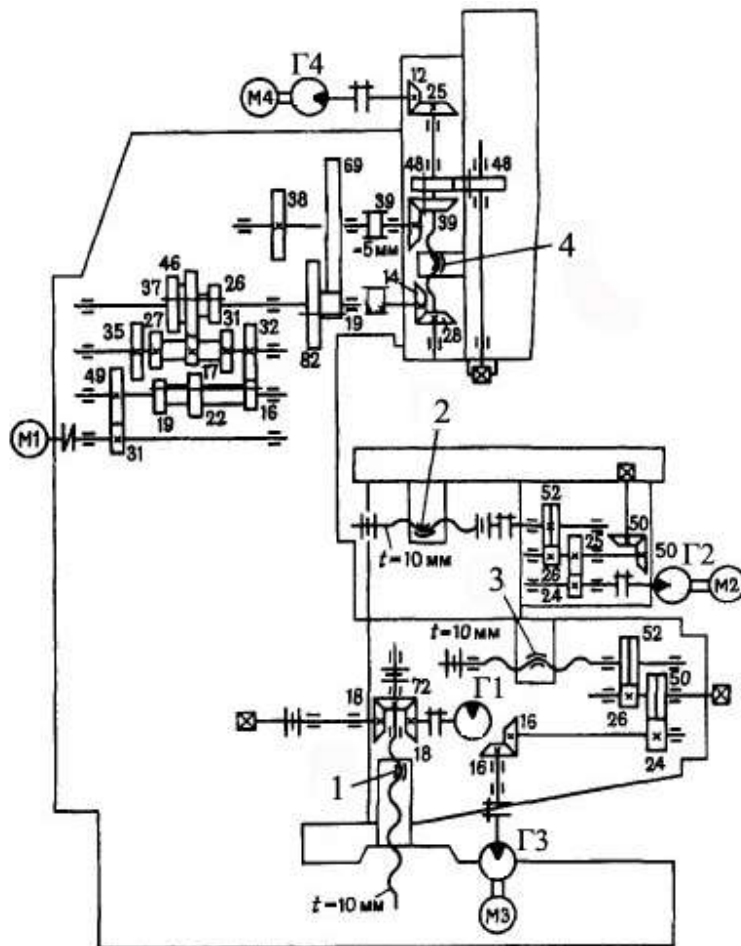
Схема вертикально-фрезерного верстата з ЧПК моделі 6P13Ф3
